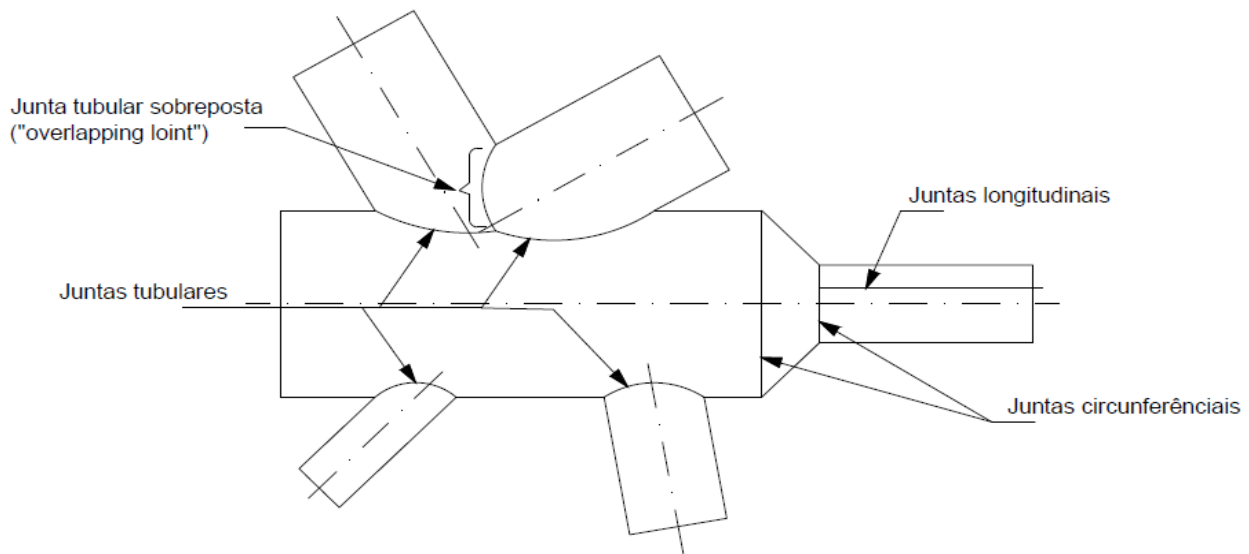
Diversos tipos de Juntas Soldadas
